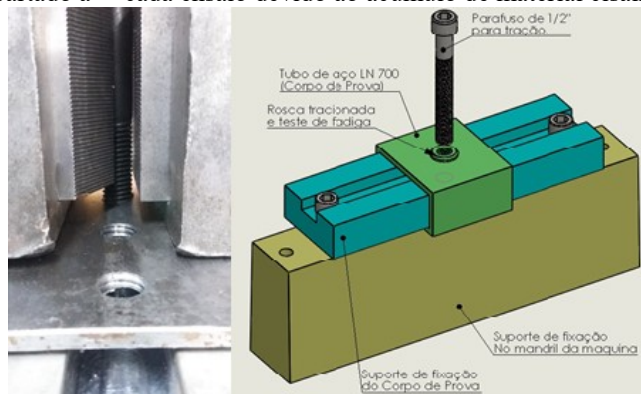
Ensaio de Tração e Dispositivo. Fonte: autores.
